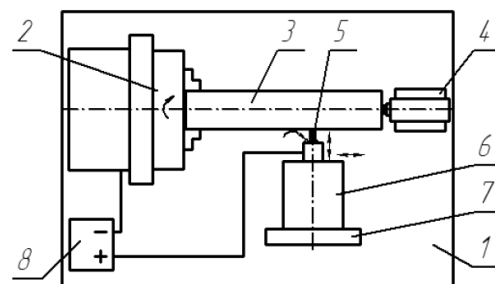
Схема установки для механізованої ЕІО: 1 – база токарного верстата; 2 – ізолюваний кулачковий патрон; 3 – оброблювана деталь; 4 – ізолювана задня бабка; 5 – легуючий електрод; 6 – механізована головка із супортом верстата; 7 – слідкувальна система; 8 – генератор імпульсів.
